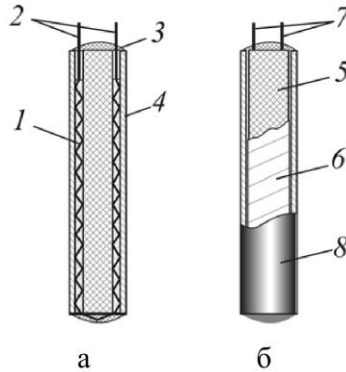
Конструкція платинового (а) і мідного (б) чутливого елементів: 1 – платинова спіраль; 2, 7 – виводи; 3 – термоцемент; 4 – металевий корпус; 5 – мідний дріт; 6 – фторопластова плівка; 8 – металева гільза
